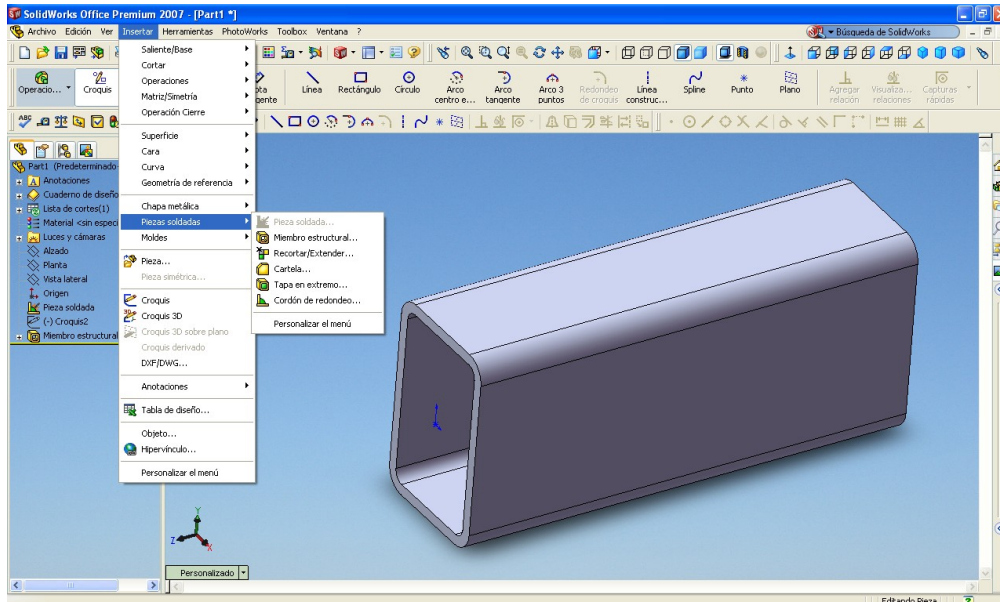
Imagen de las operaciones del Subentorno Soldadura
